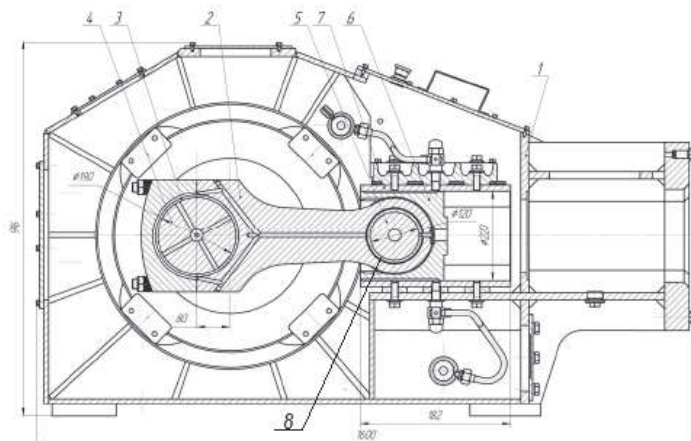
Основные элементы конструкции шатунно-крейцкопфного механизма привода плунжерного насоса высокого давления: 1 – корпус приводной части насоса; 2 – шатун; 3 – вкладыш; 4 – вал кривошипный; 5 – палец шатуна; 6 – крейцкопф; 7 – направляющие 8- втулка
